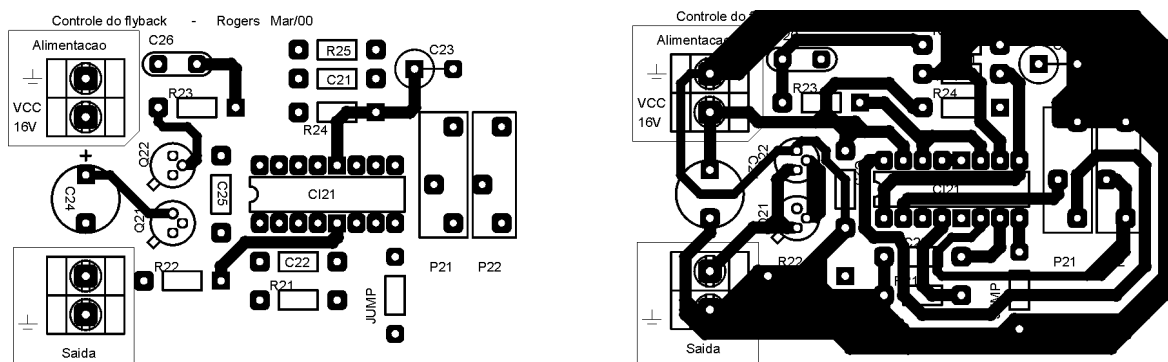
Placa de circuito impresso do conversor flyback.
